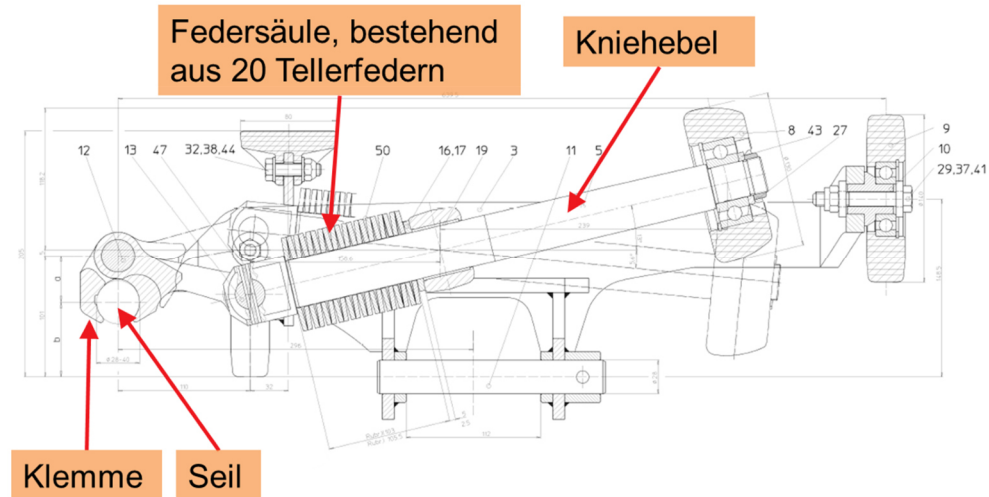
Technische Zeichnung der Seilklemme Typ AK 2.1
